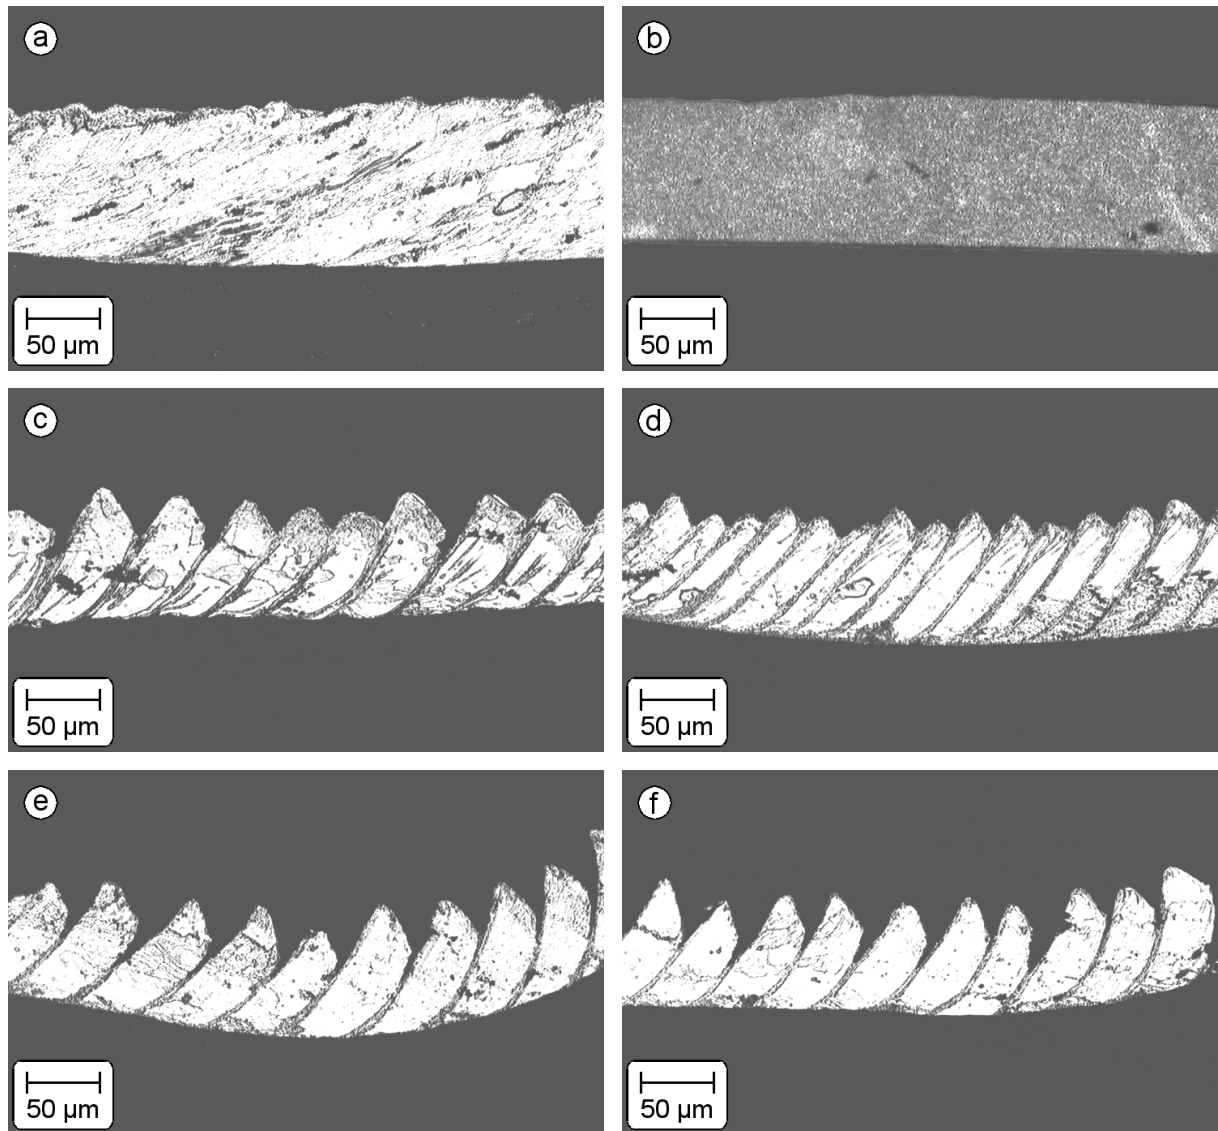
Lichtmikroskopische Aufnahmen der Späne unterschiedlicher Gefüge der Aluminiumlegierung 7050 ($f_z = 0,2 \text{ mm}$): (a) lösungsgeglüht, $v_c = 7000 \text{ m/min}$; (b) T 7, $v_c = 7000 \text{ m/min}$; (c) T 4 K, $v_c = 7000 \text{ m/min}$; (d) T 4 W, $v_c = 1000 \text{ m/min}$; (e) T 4 W, $v_c = 3000 \text{ m/min}$; (f) T 6, $v_c = 4000 \text{ m/min}$
